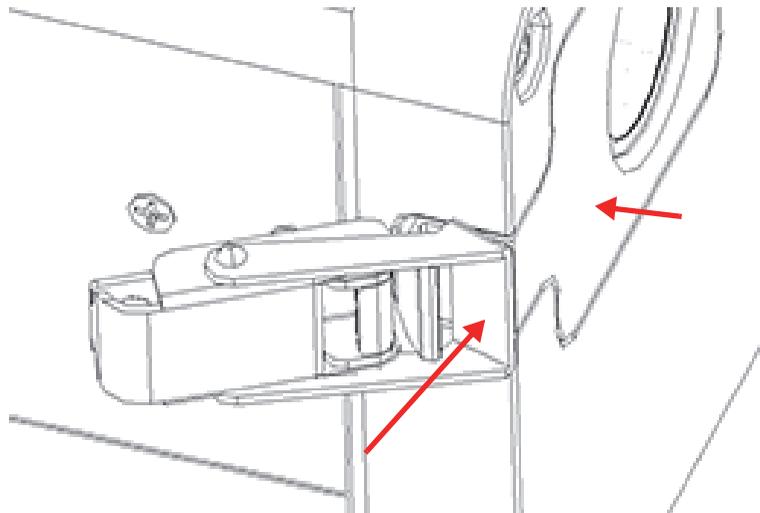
Bouton d'ouverture sur la prise de la plaque frontale
